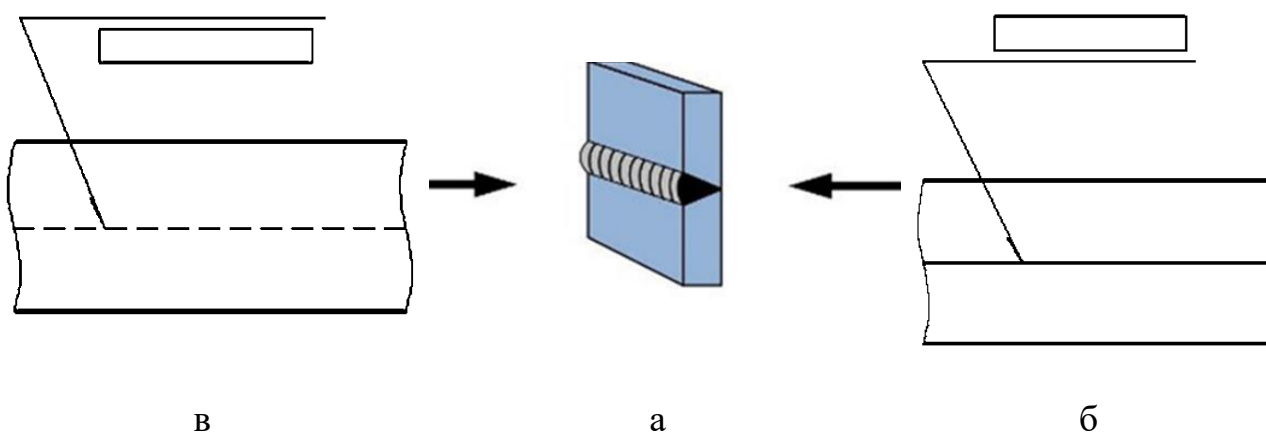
Образец схемы нанесения условного обозначения сварного шва
